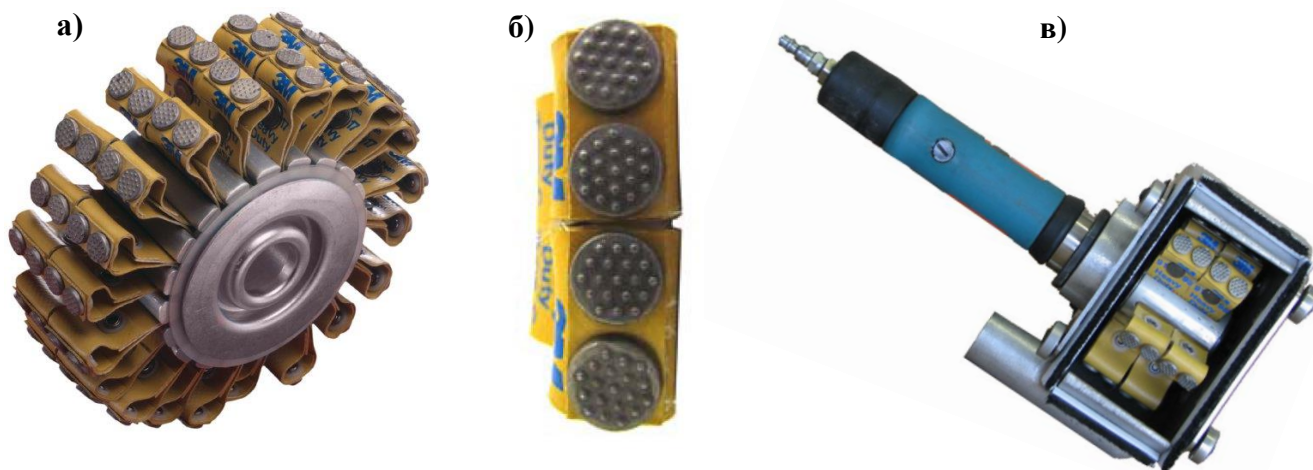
Высокопроизводительный роторно-ударный инструмент: а – роторно-ударная головка с гибкими лепестками; б – ударные элементы, армированные твердосплавными зубками; в – прямая шлифмашина в пневмоприводном исполнении типа Roto-Peen с устройством для отвода пыли.
